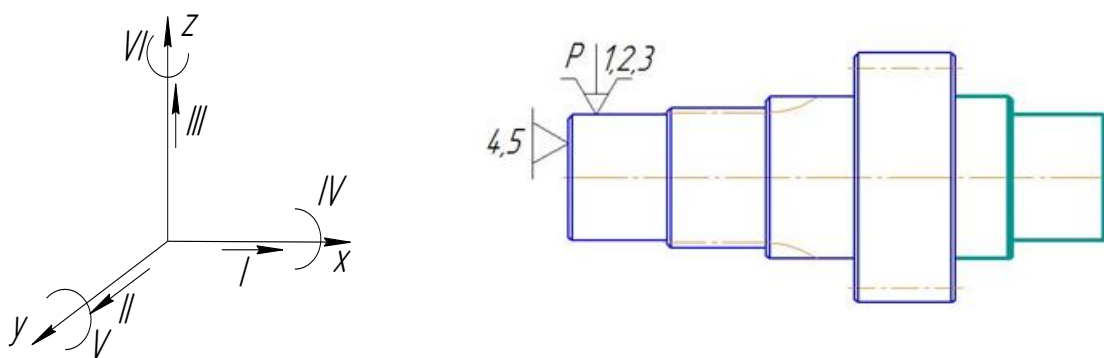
Ескіз обробки заготовки на операції 050
